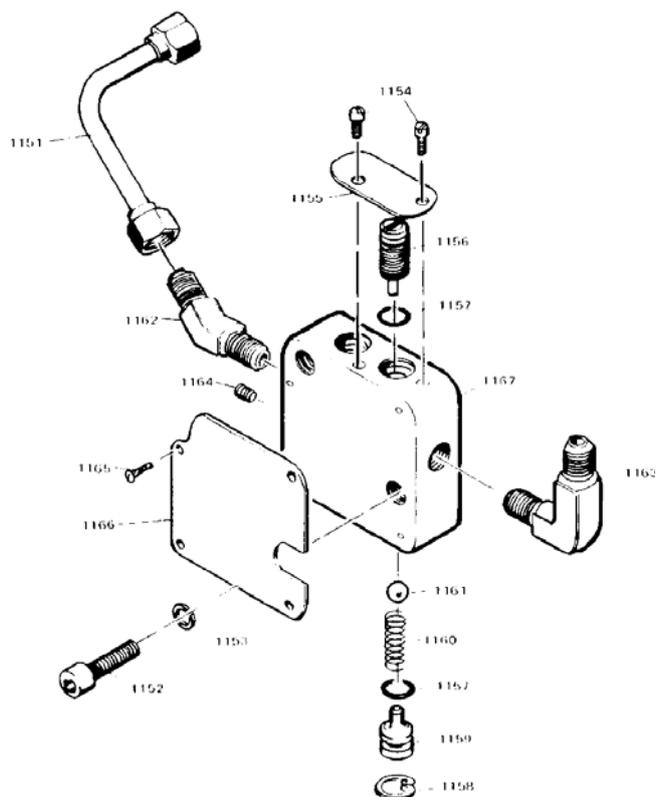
Покомпонентный чертеж сборки распределительного клапана лопастного сервопривода (внешнего типа)
